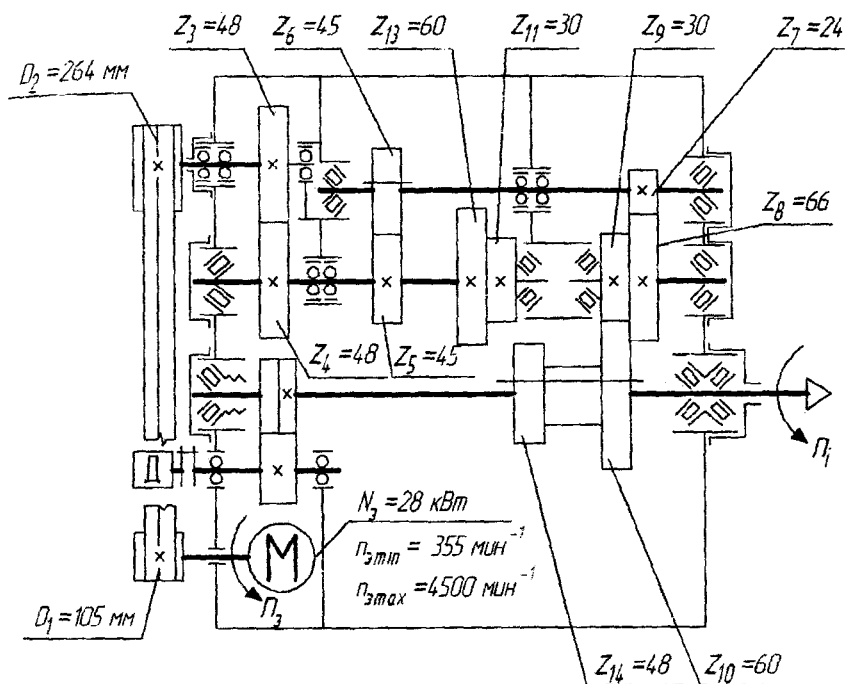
Кинематическая схема главного привода токарного станка с ЧПУ модели 16К20Ф3
